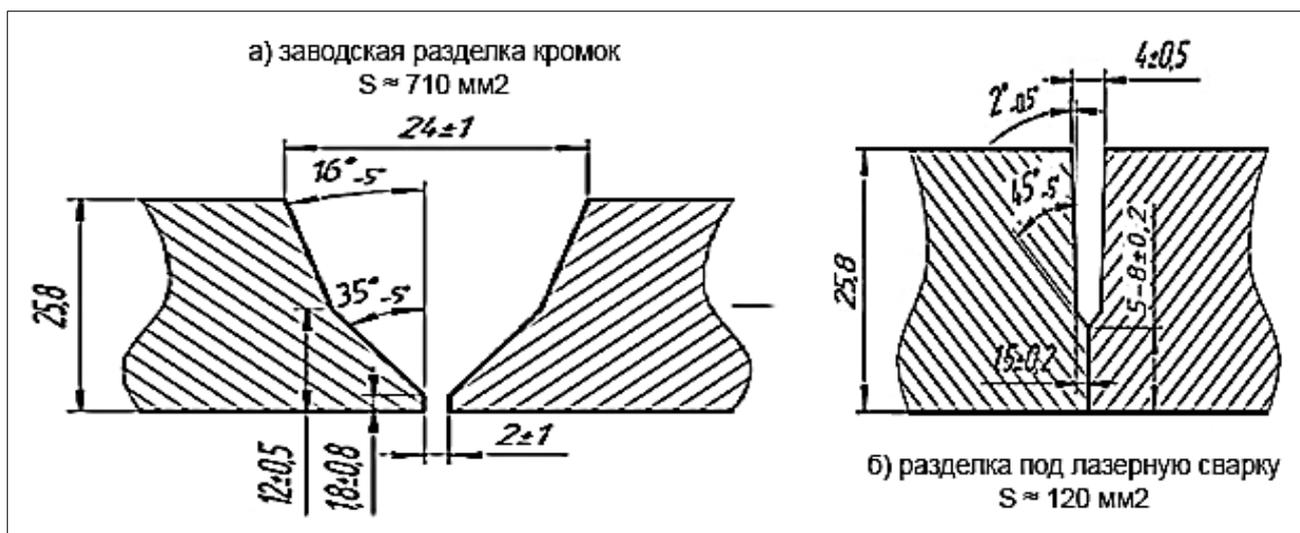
Разделка свариваемых кромок а) под электродуговую сварку и б) под лазерную сварку
